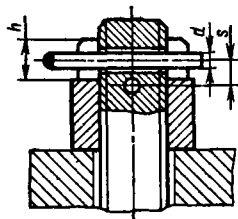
Способ шплинтовки с увеличенным ходом гайки
